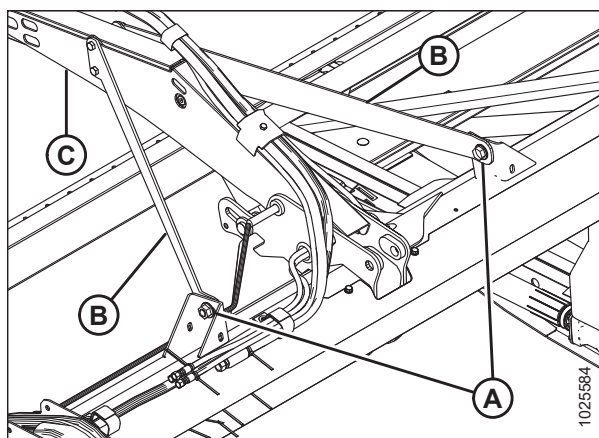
Центральный опорный рычаг мотовила — конфигурация для стран Северной Америки
